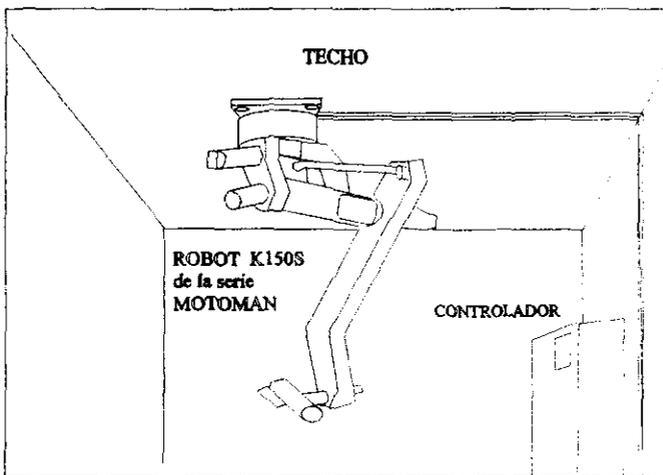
ROBOT DISEÑADO PARA SER MONTADO EN EL TECHO.
